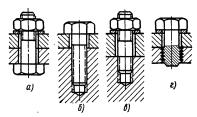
Основные типы резьбовых соединений: a — болтом (винтом с гайкой); s — винтом; s — шпилькой с гайкой; s — винтом с вставкой
